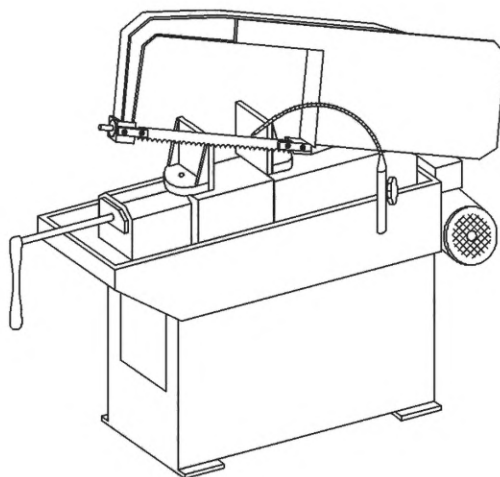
Приводные ножовки — горизонтально-поворотный тип
